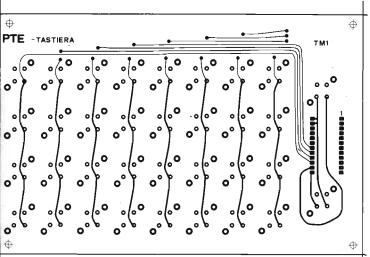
a-b - Disegno del circuito stampato della tastiera TM1.
